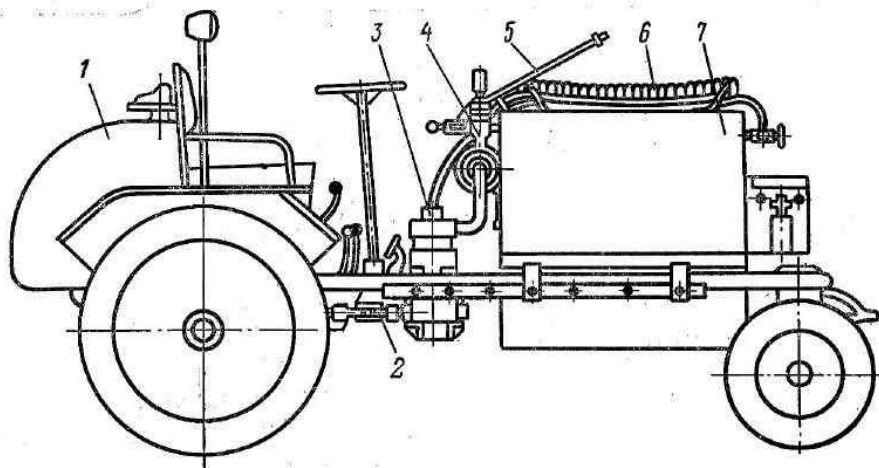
Установка для профилактической обработки рыбы ПАО:
